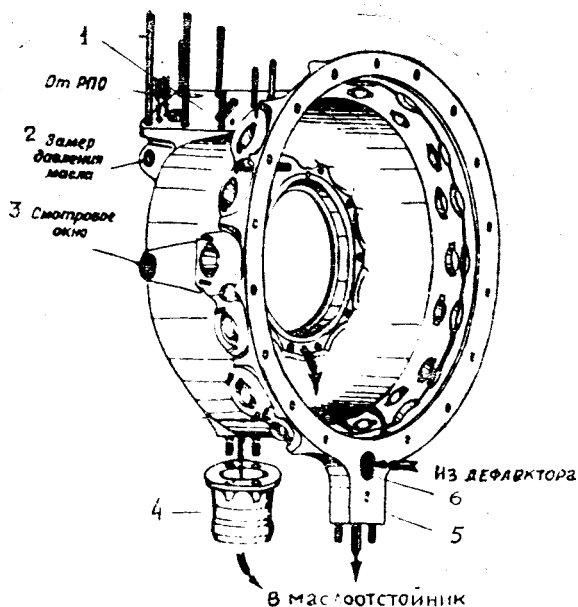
Носок картера: 1—фланец привода РПО; 2—гнездо замера давления масла; 3—смотровое окно; 4—труба слива масла в маслосборник; 5—установка переднего фланца маслосборника; 6—гнездо установки дефлектора
